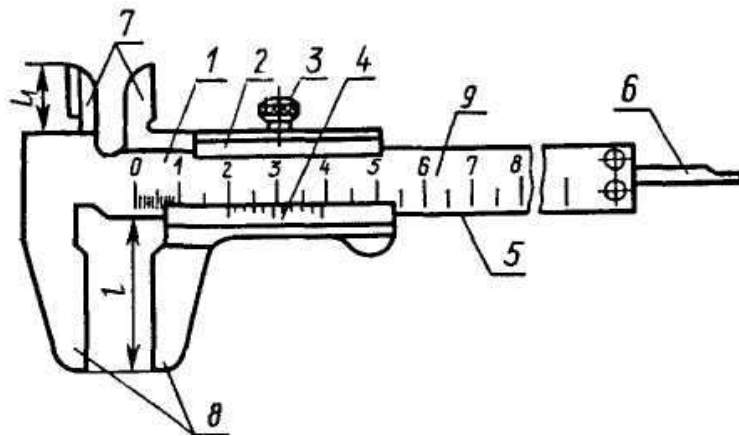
1 – штанга; 2 – рамка; 3 – затискувач; 4 – ноніус; 5 – робоча поверхня штанги; 6 – глибиномір; 7 – губки з кромковими вимірювальними поверхнями для вимірювання внутрішніх розмірів; 8 – губки з плоскими вимірювальними поверхнями для вимірювання зовнішніх розмірів; 9 – шкала штанги
